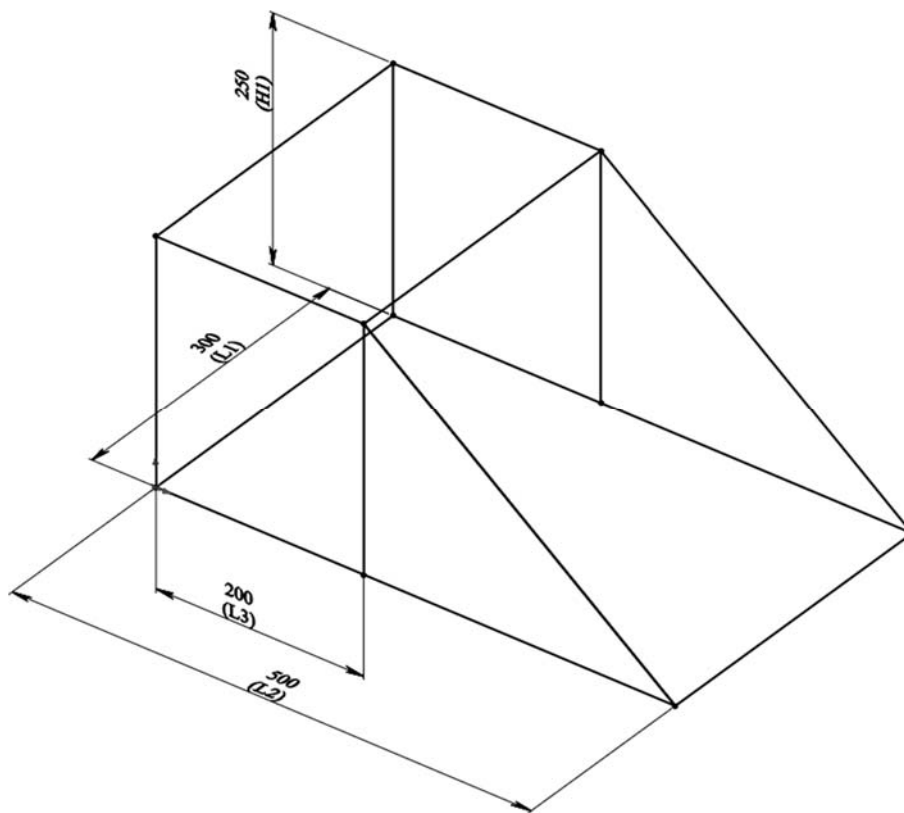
3D-эскиз сварного изделия
